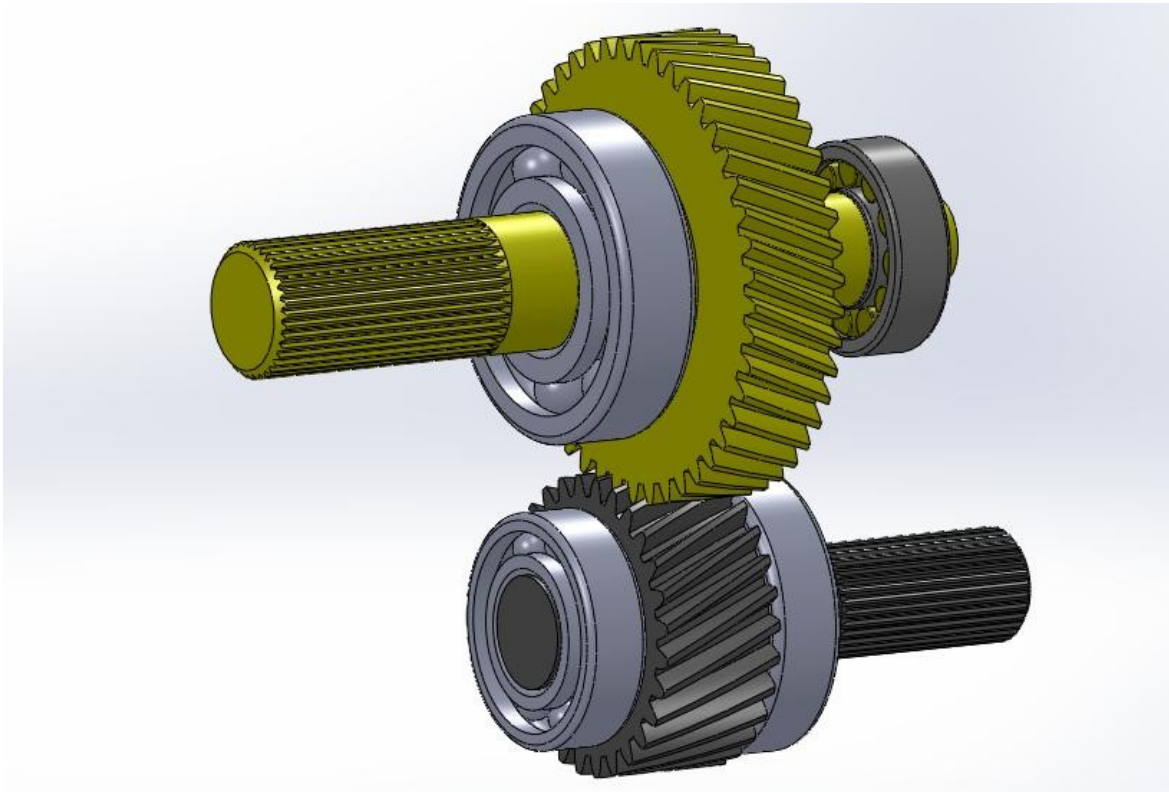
e 2.10 – Assemblaggio degli alberi comprensivi di cuscinetti –
